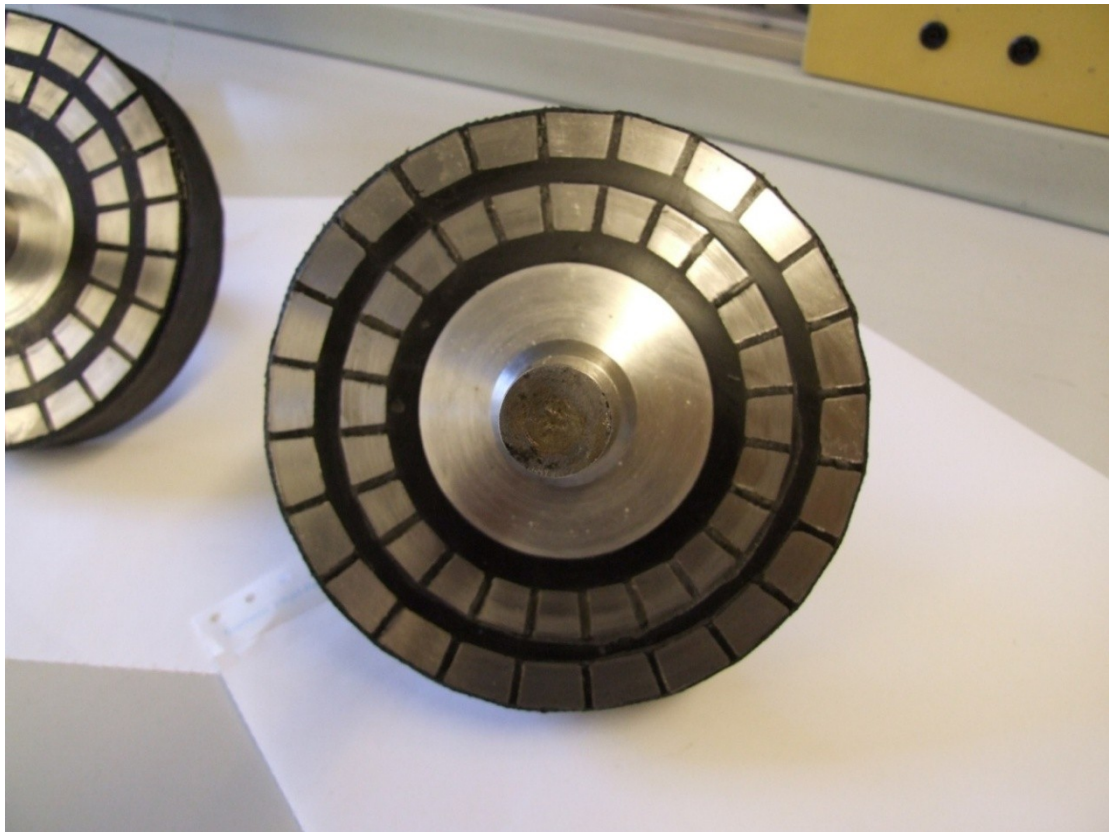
Foto eines Rotors in axialer Richtung
